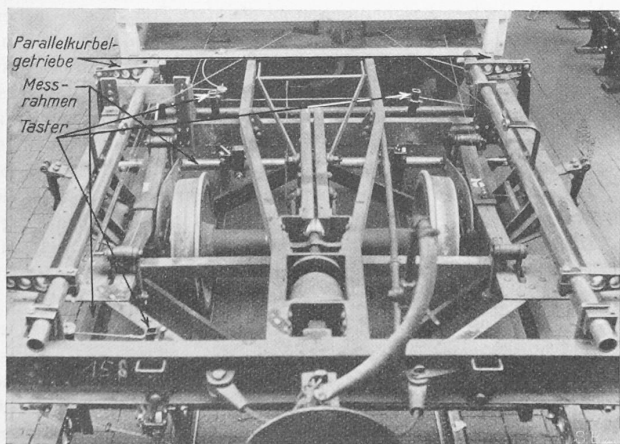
Draufsicht auf die Amslersche Messvorrichtung.
